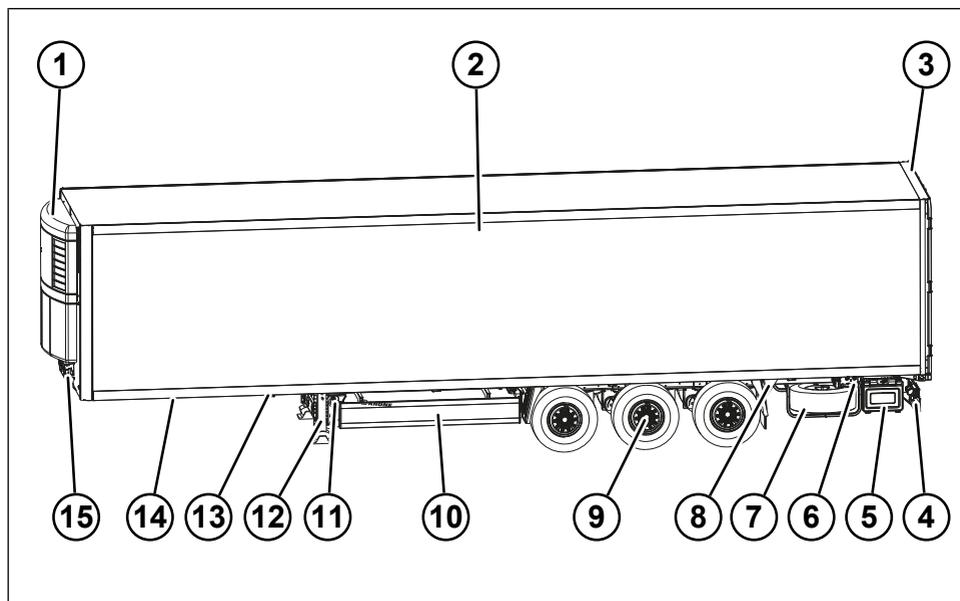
Vista de conjunto do Cool Liner (exemplo)
